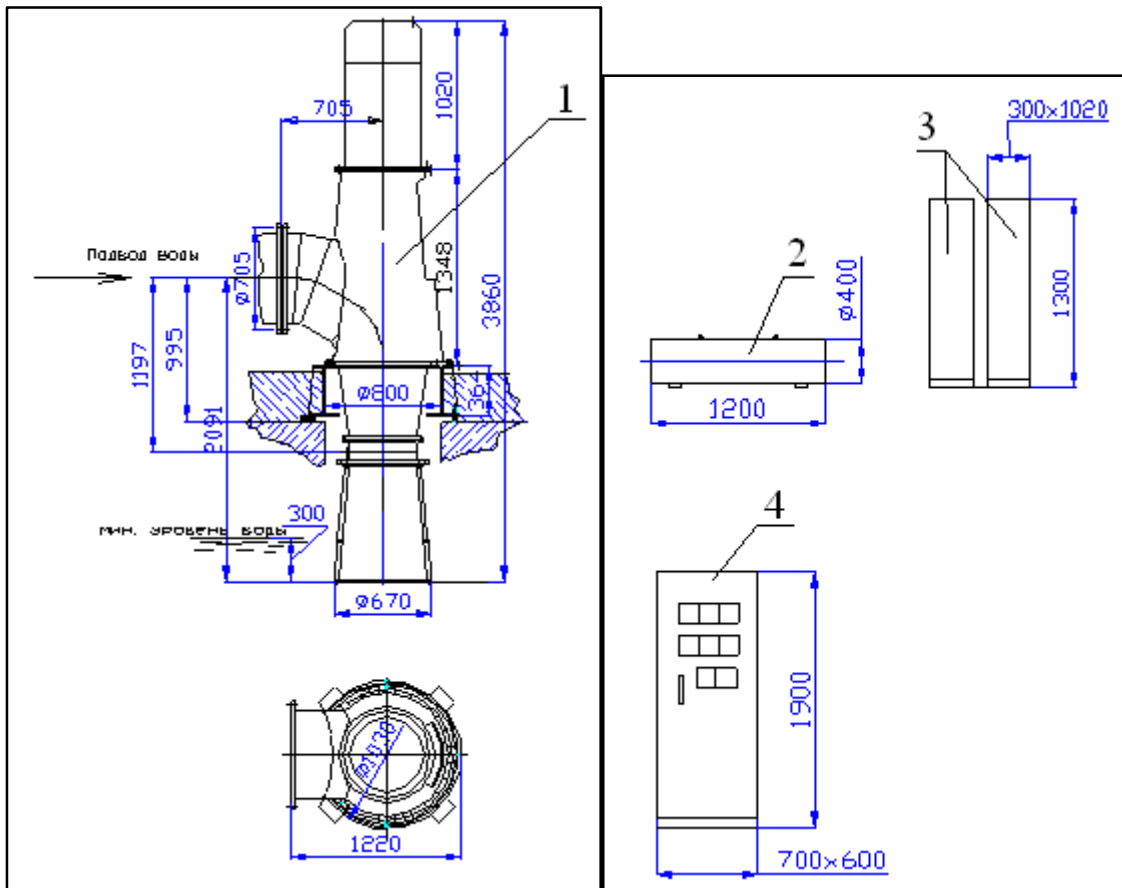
Габаритные, установочные и присоединительные размеры микроГЭС 50Pr вертикального исполнения:
